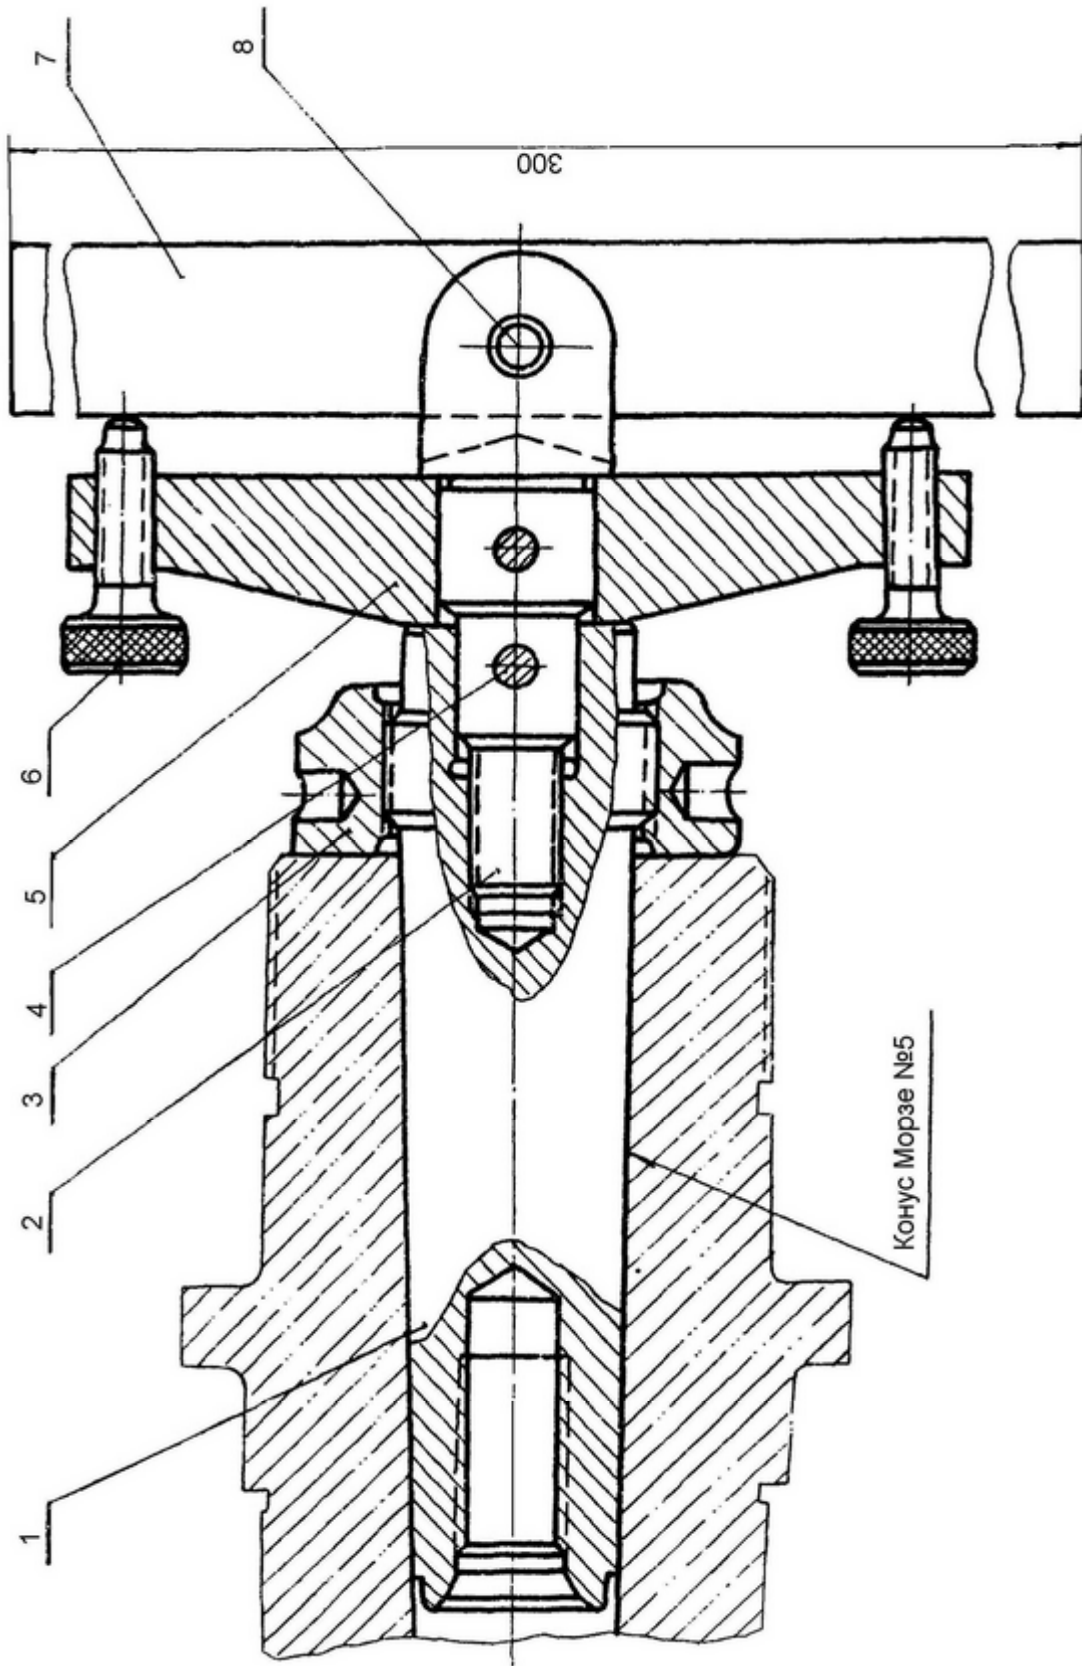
Приспособление для проверки перпендикулярности оси шпинделя к направляющим поперечного суппорта СД 8532 – 4005
